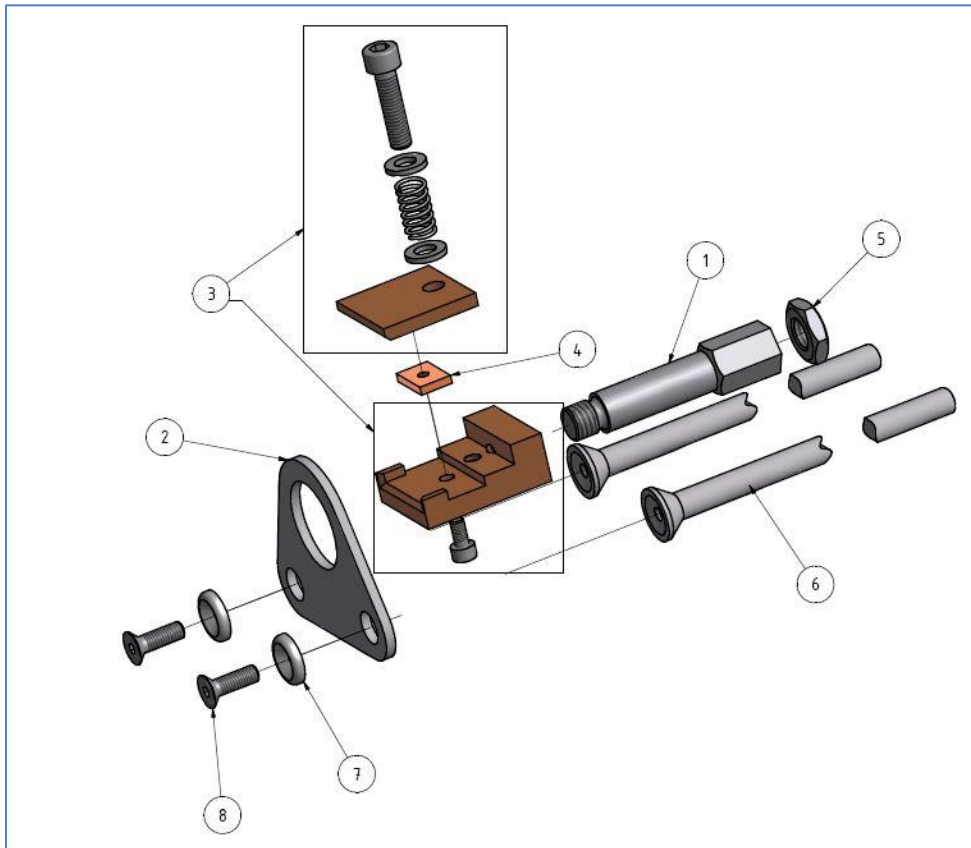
Stützeinrichtung für das Schutzgasbolzenschweißen (Pistole K 22)
